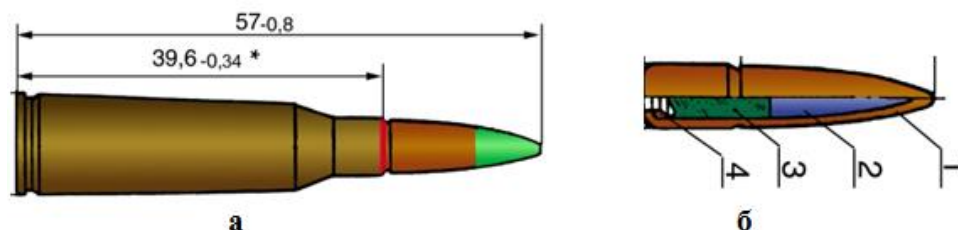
а – патрон, б – пуля; 1 – оболочка; 2 – сердечник свинцовый; 3 – трассер; 4 – колечко
